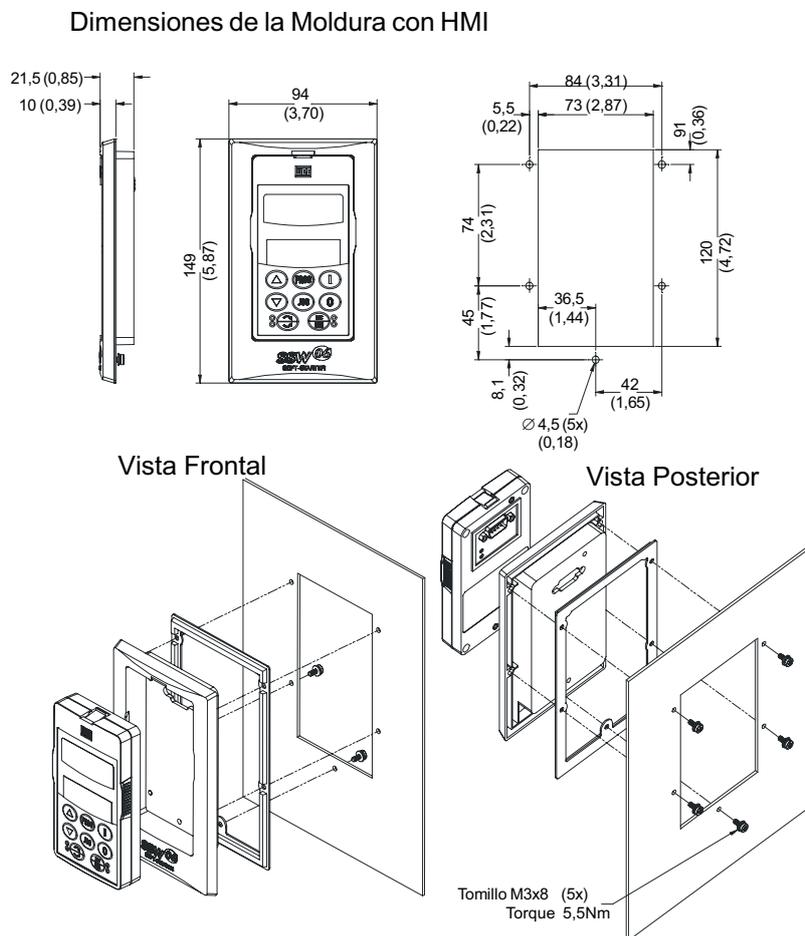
Dimensiones en mm (in) y como instalar la HMI y Moldura en el panel
